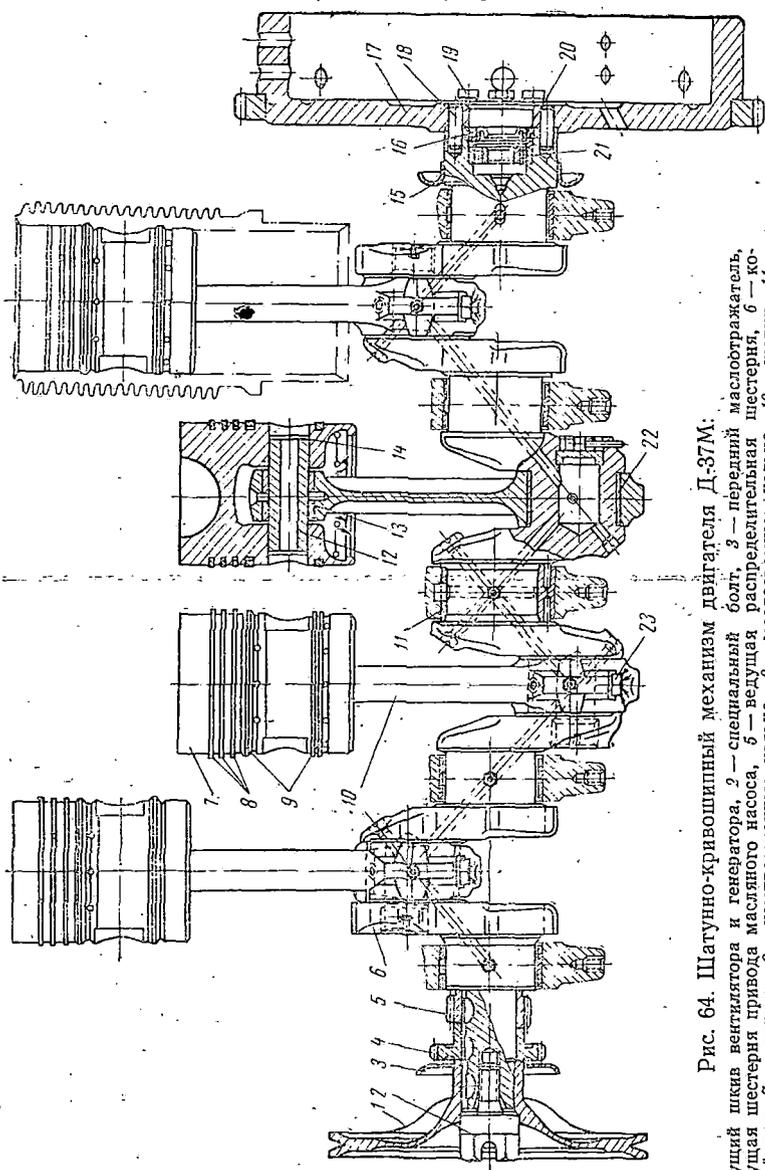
Шатунно-кривошипный механизм двигателя Д-37М:
